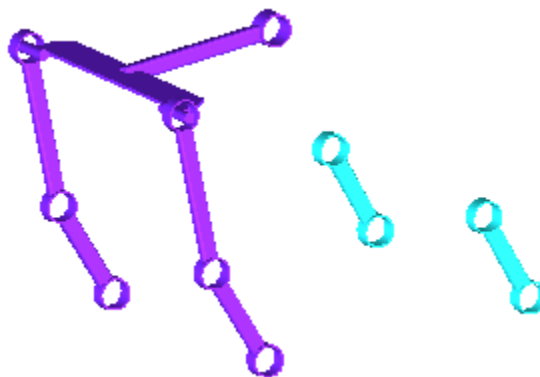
Conjunto soldado para la tracción del prototipo.
